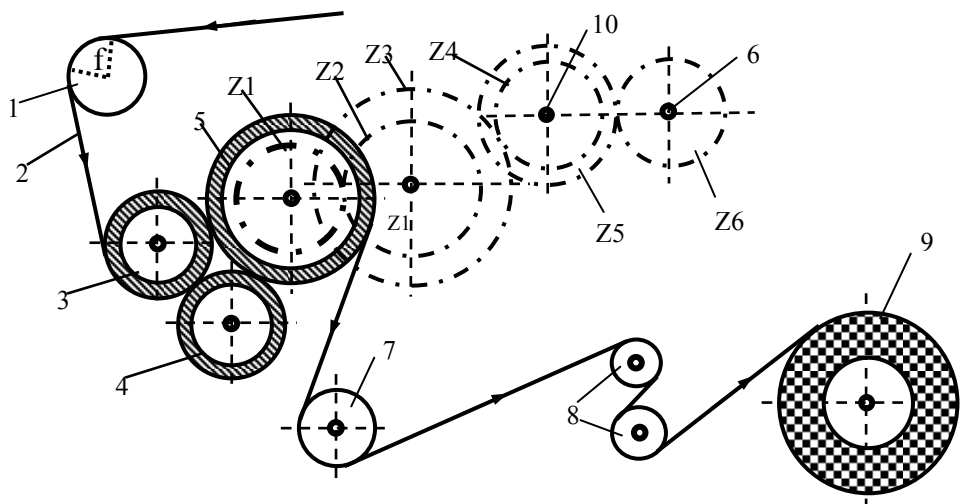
Regulatorul pozitiv pe mașina de țesut hidraulică
